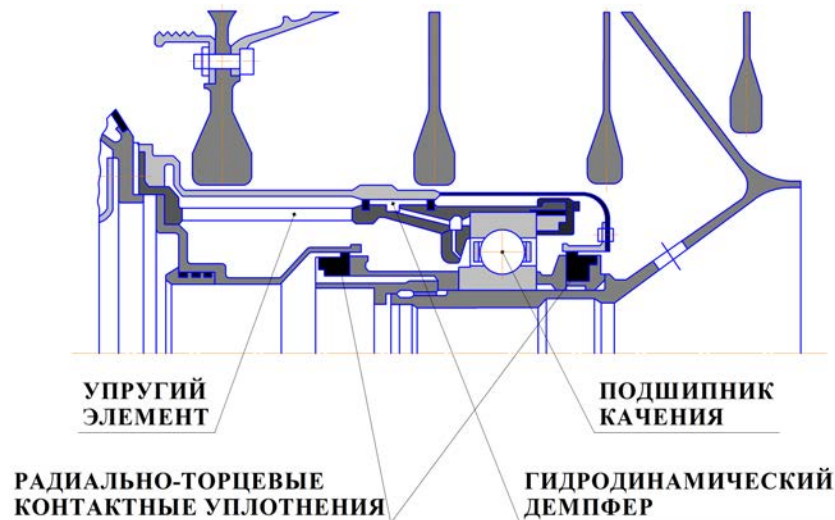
Схема передней опоры ротора компрессора низкого давления двигателя Д-36
